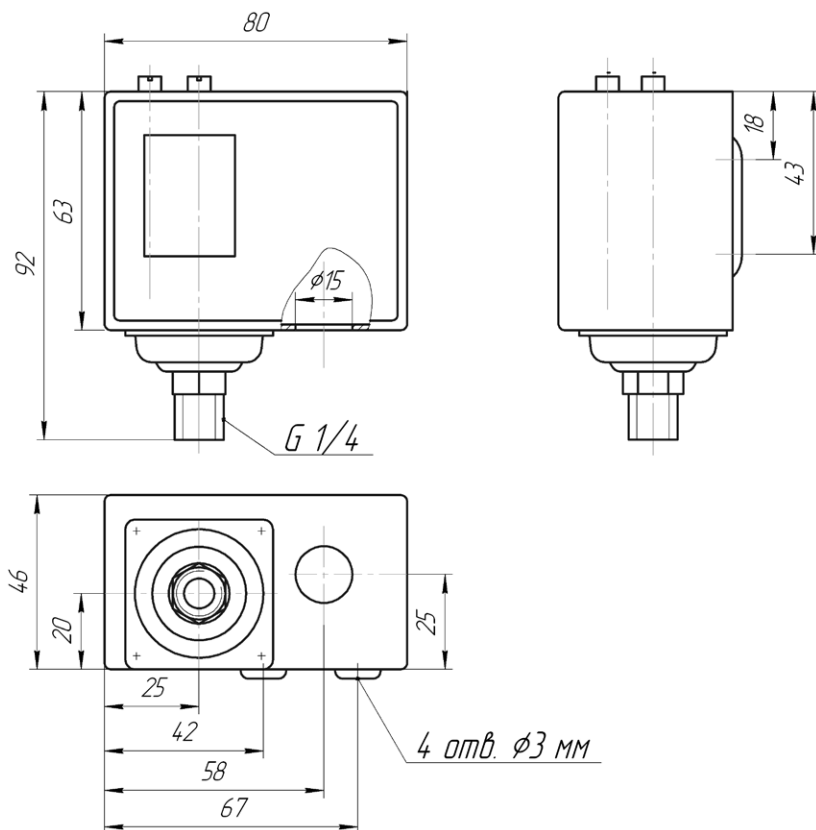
Габаритные и установочные размеры датчика-реле давления
